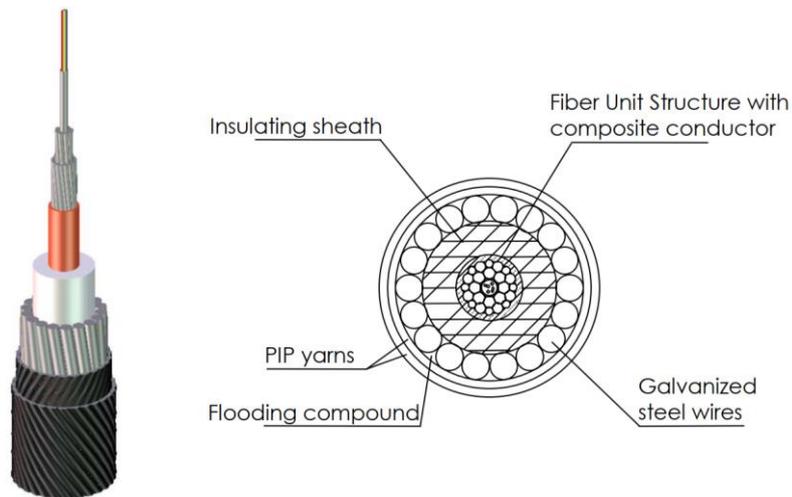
Vue éclatée et coupe transversale du câble SA (ASN)
